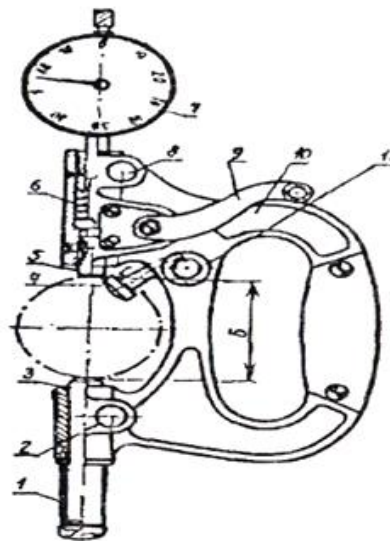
Індикаторна скоба: 1 - захисний ковпачок; 2 - стопорний гвинт; 3 - переставна п'ятка; 4 - упорна п'ятка; 5 - рухома п'ятка; 6 - пружина; 7 - індикатор; 8 - стопорний гвинт; 9- відвідний важіль (аретир); 10 - корпус; 11 - стопор упорної п'ятки
